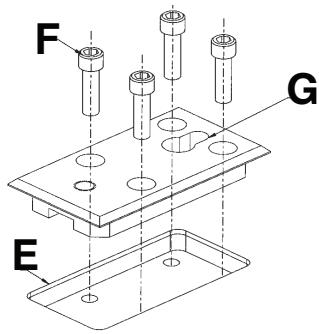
Anclaje de la placa de suelo y puntos de posicionamiento
